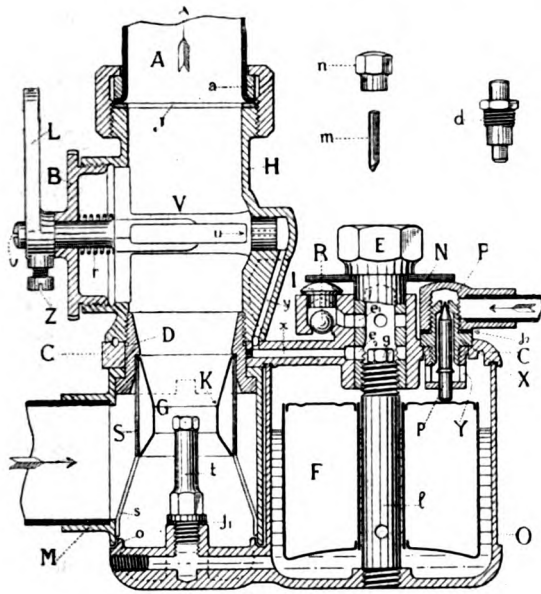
COUPE DU CARBURATEUR SOLEX.
